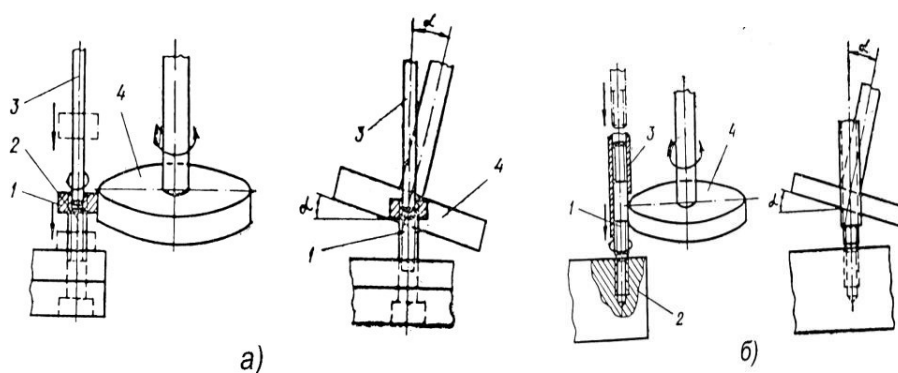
Фрикційно-інерційний спосіб загвинчування: а- гайок: 1- гайка; 2-болт; 3- напрямний стержень; б-шпильок: 1- шпилька; 2- корпус; 3- напрямна втулка.
